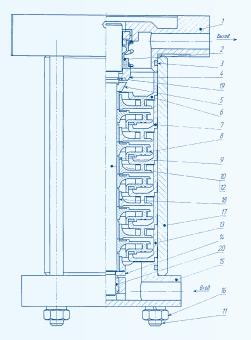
Насос центробежный: 1 – фланец верхний; 2 – торцовое уплот– нение; 3 – кольцо уплотнительное; 4, 5 – диск; 6, 7, 13 – аппарат направляющий; 8 – колесо рабочее; 9 – втулка; 10 – вал; 11 – шпилька; 12 – шпонка; 14 – диск; 15 – фланец нижний; 16 – гайка; 17 – гильза; 18 – втулка; 19 - кольцо стопорное; 20 - втулка
